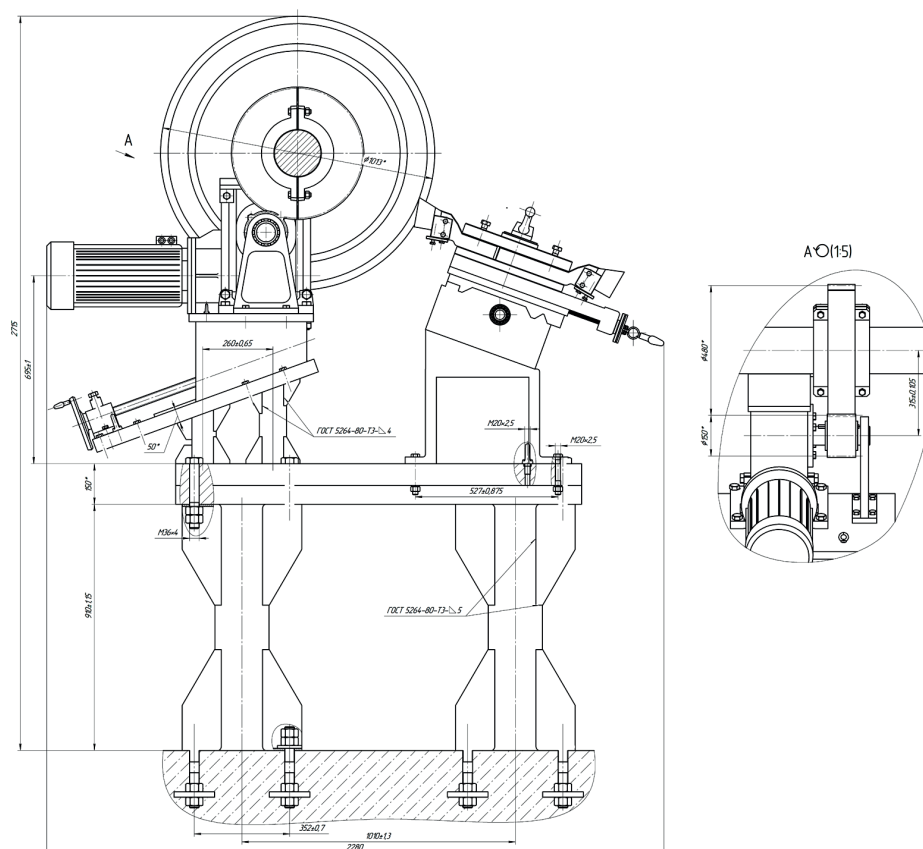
Устройство для обработки колесных пар в сборе [2]
